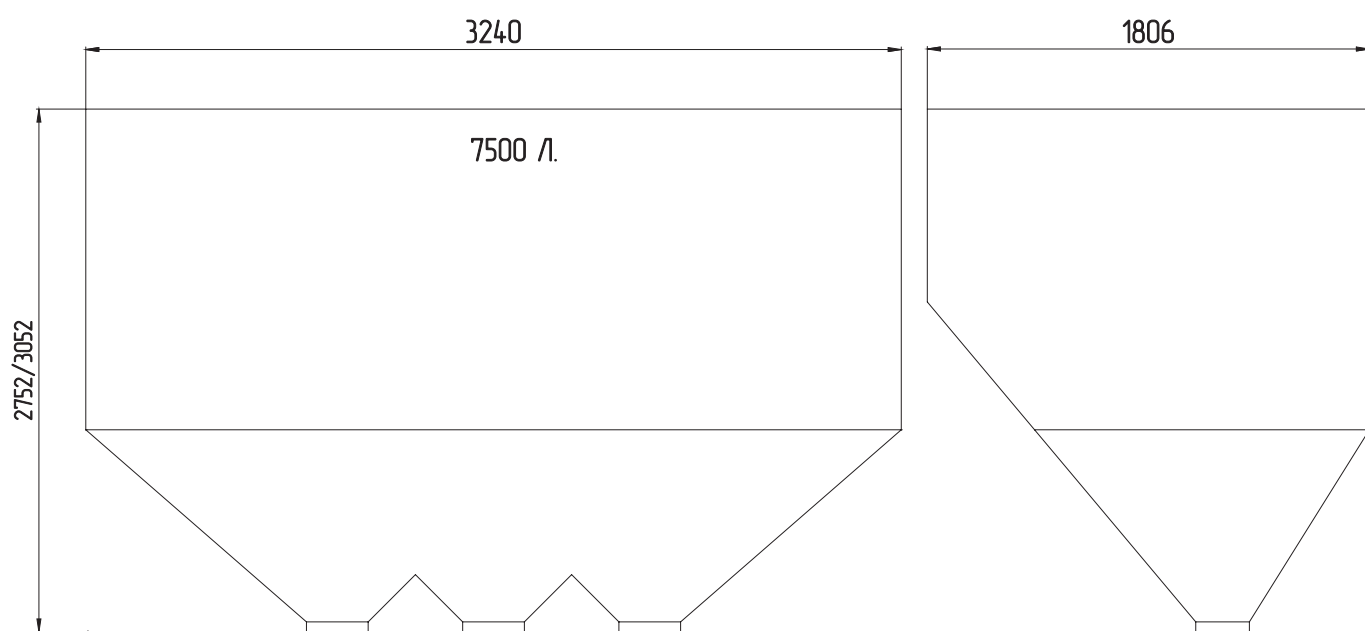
Габаритные размеры топливного бункера 7500 л 3 горла
